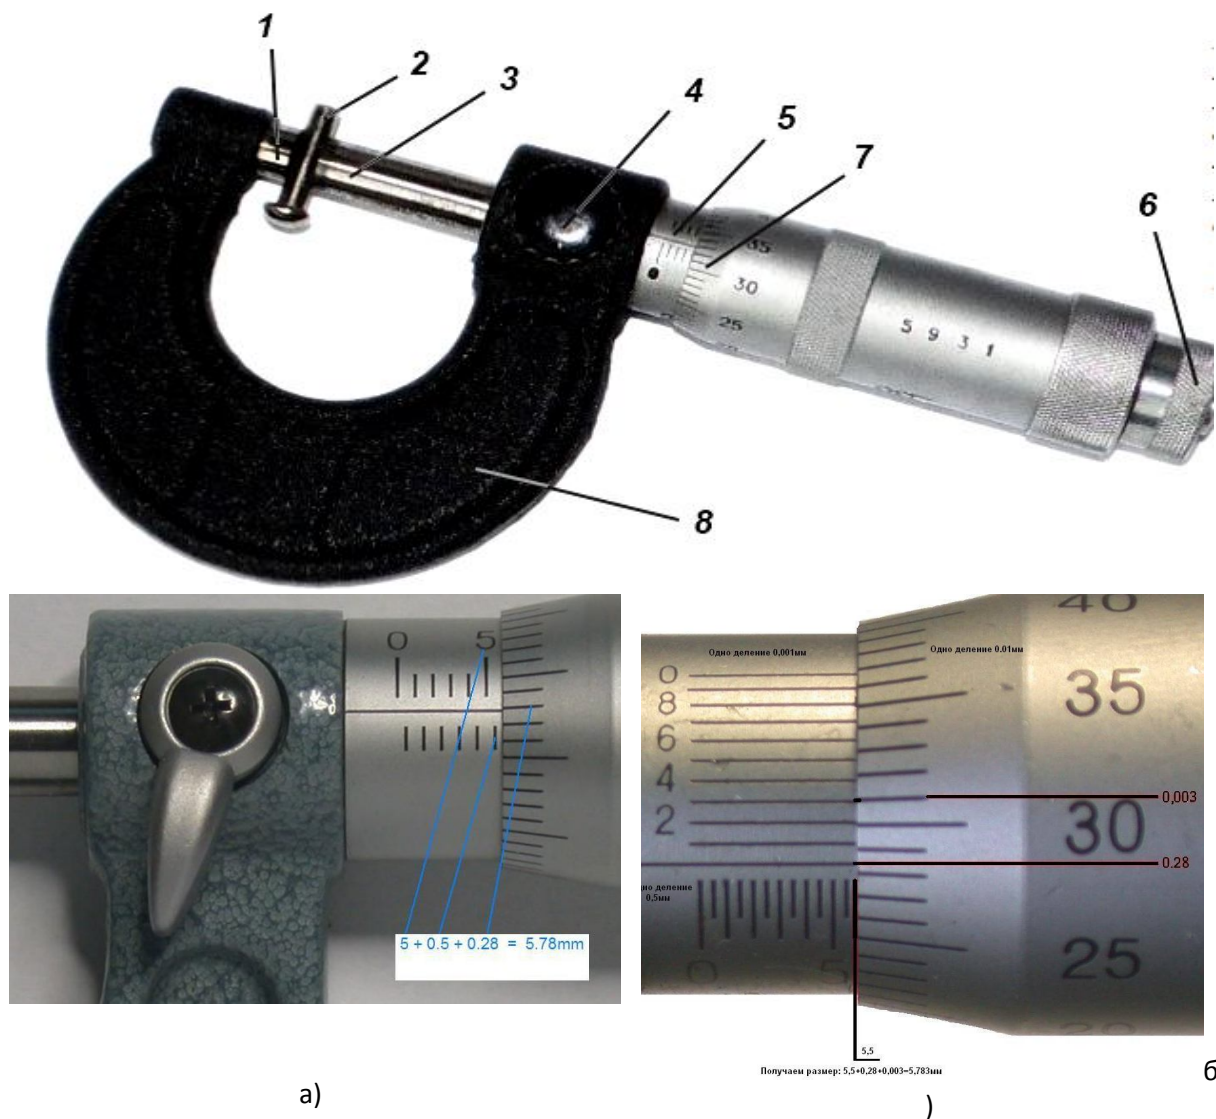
Устройство и принцип работы с микрометром: 1 – пятка; 2 – измеряемый предмет; 3 – шпindelь микрометрического винта; 4 – стопор микрометрического винта; 5 – горизонтальная шкала; 6 – трещотка; 7 – барабан с круговой шкалой; 8 – скоба
